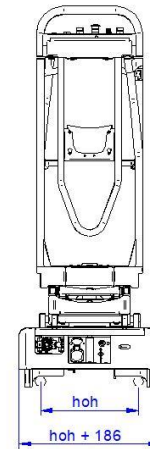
; Dimensions de la largeur en mm, 2 pantographes
